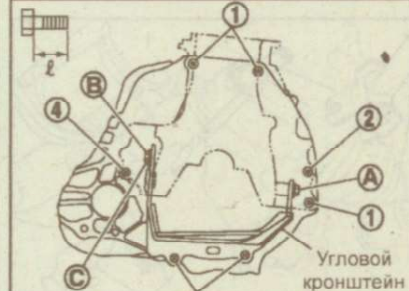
Расположение болтов крепления коробки передач RS5F70A
